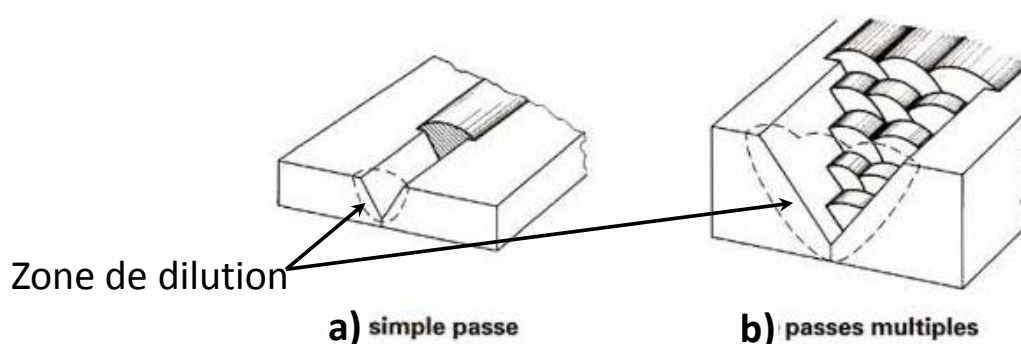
Illustration de différentes configurations de soudage de deux pièces : (a) simple passe (b) passes multiples [93]
